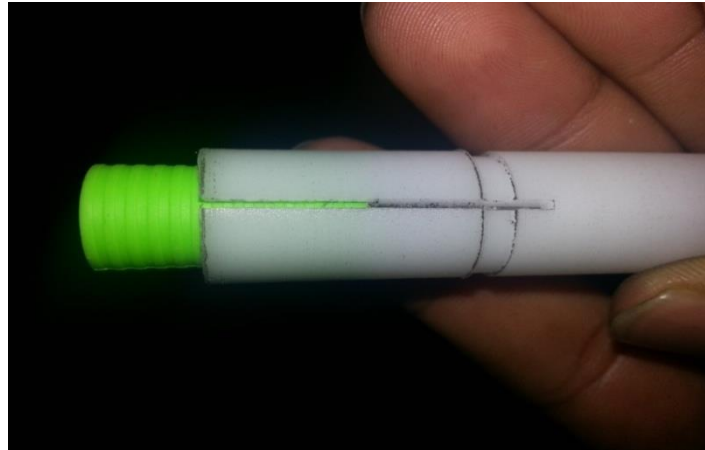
Fixture terminada con Grip colocado en su cavidad interior.
